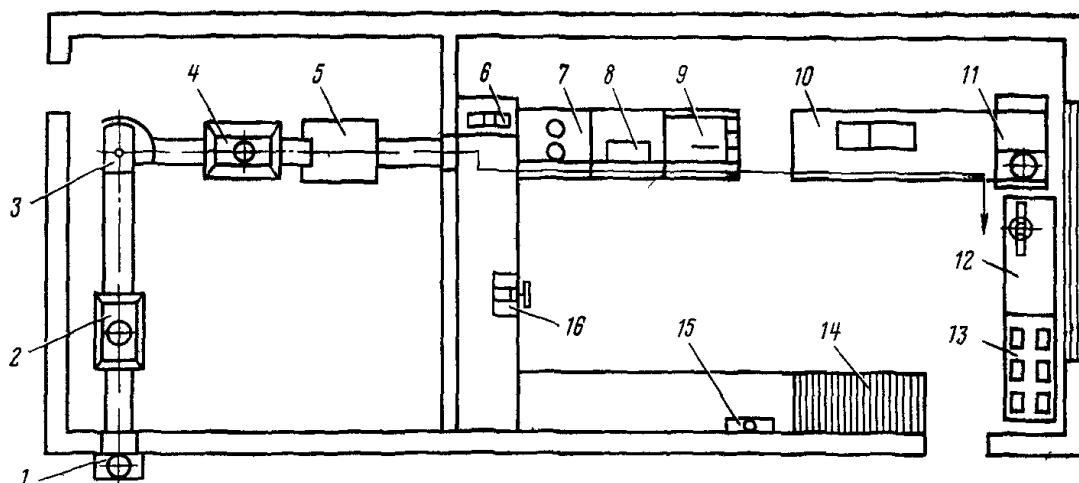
Планировка поточной линии ремонта роликовых подшипников в депо
